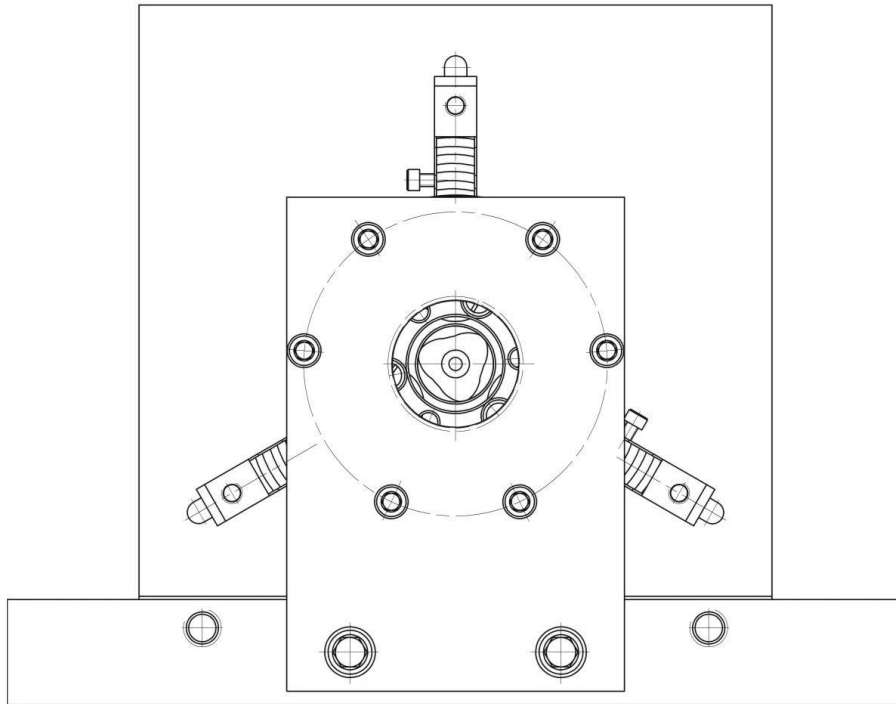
Трироликівка обкатна головка (вид Г)
